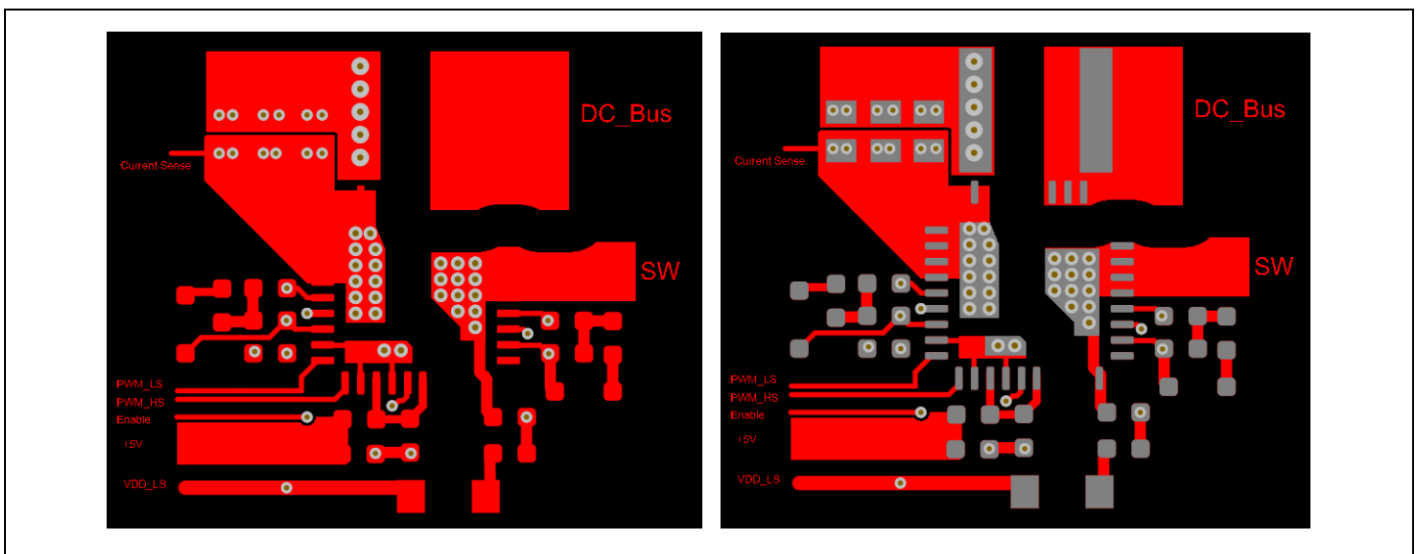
PCB 顶层（左侧为走线，右侧为顶部焊膏层）
